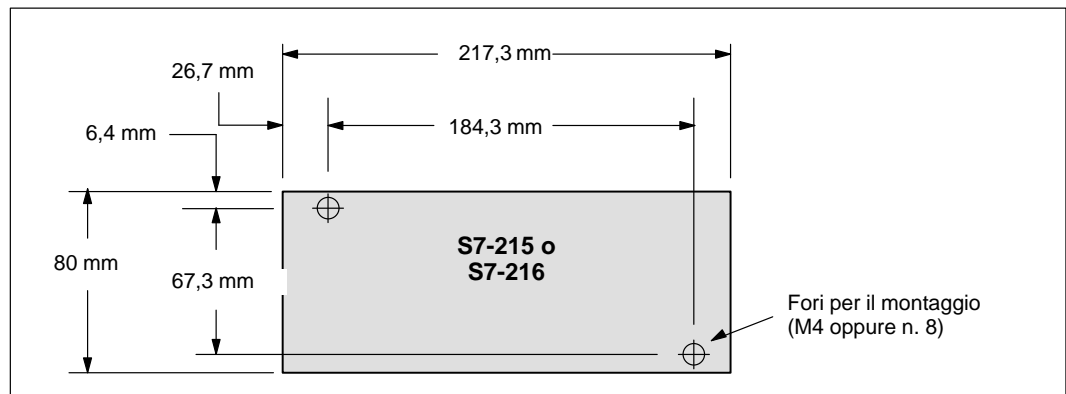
Dimensioni per il montaggio di CPU S7-215 e CPU S7-216
